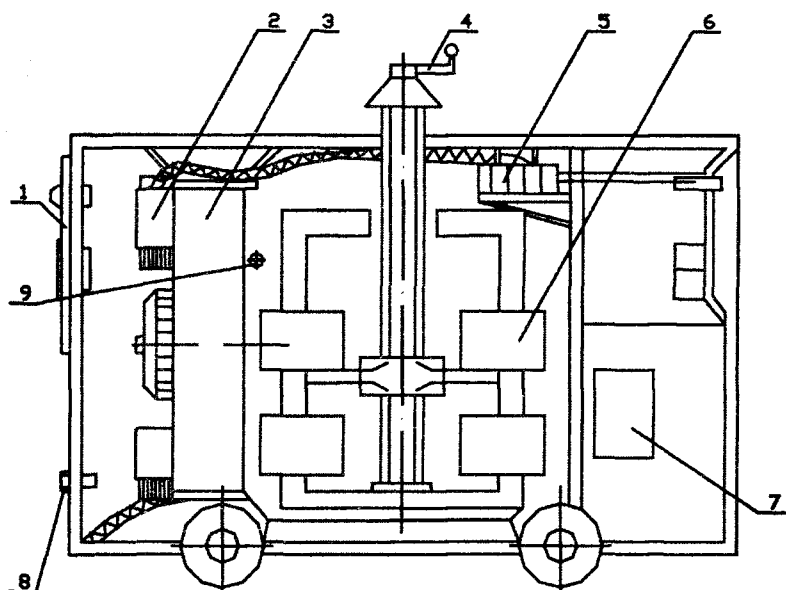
Конструктивная схема сварочного выпрямителя ВД-306УЗ. 1- панель управления, 2- блок силовых вентилялей, 3- вентилятор, 4 - рукоятка перемещения обмоток, 5 - переключатель диапазонов силы сварочного тока, 6- трансформатор, 7- силовой блок системы управления, 8 - выводы для подключения сварочных проводов, 9 - реле потока воздуха
